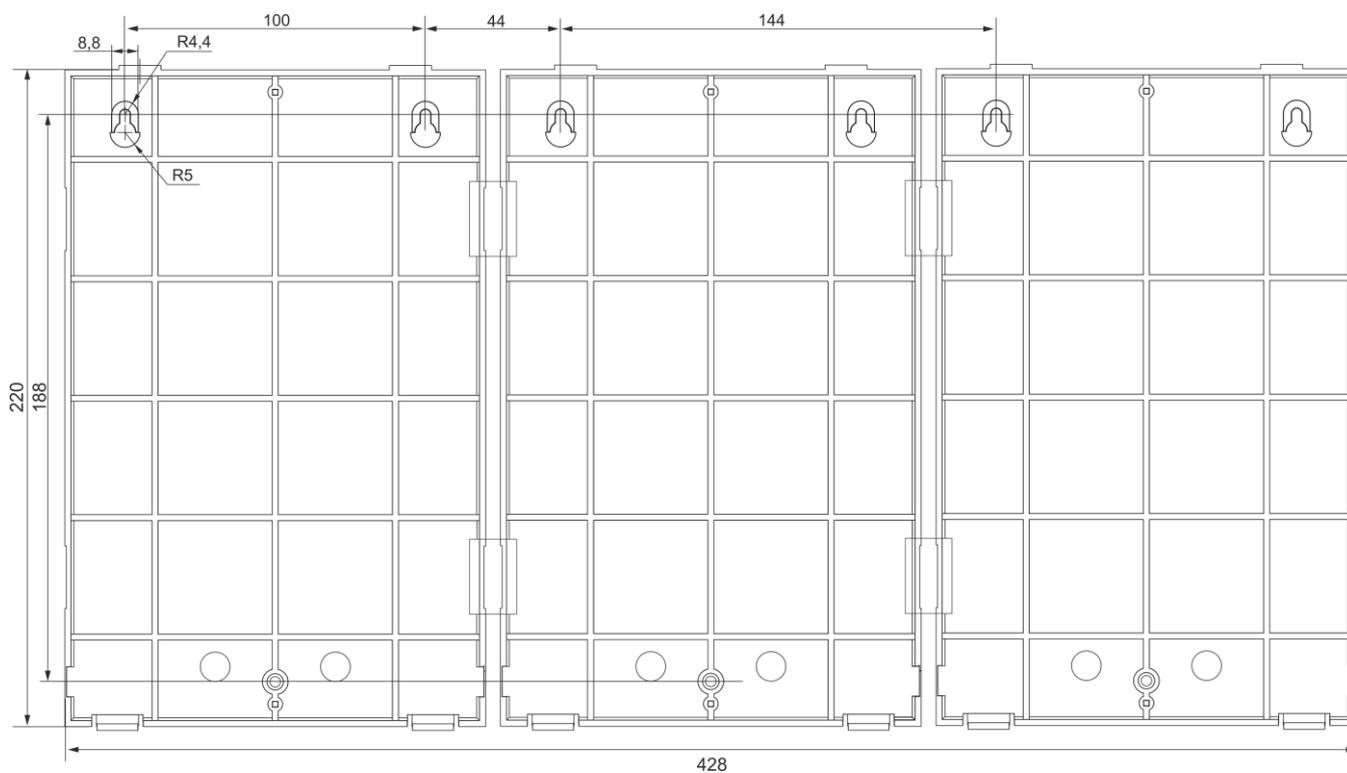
Установочный чертеж основания корпуса ВПУ-А24/700
